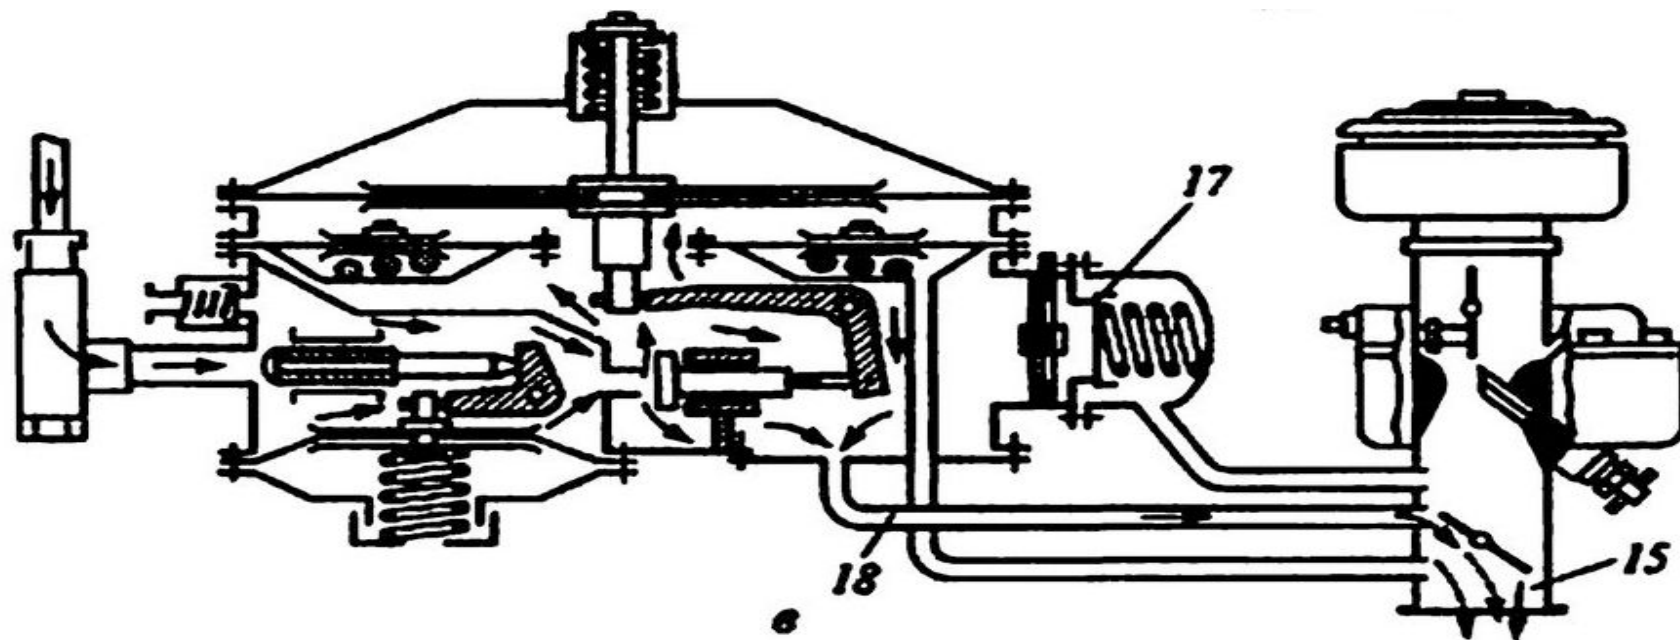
Схема работы двухступенчатого газового редуктора низкого давления:
